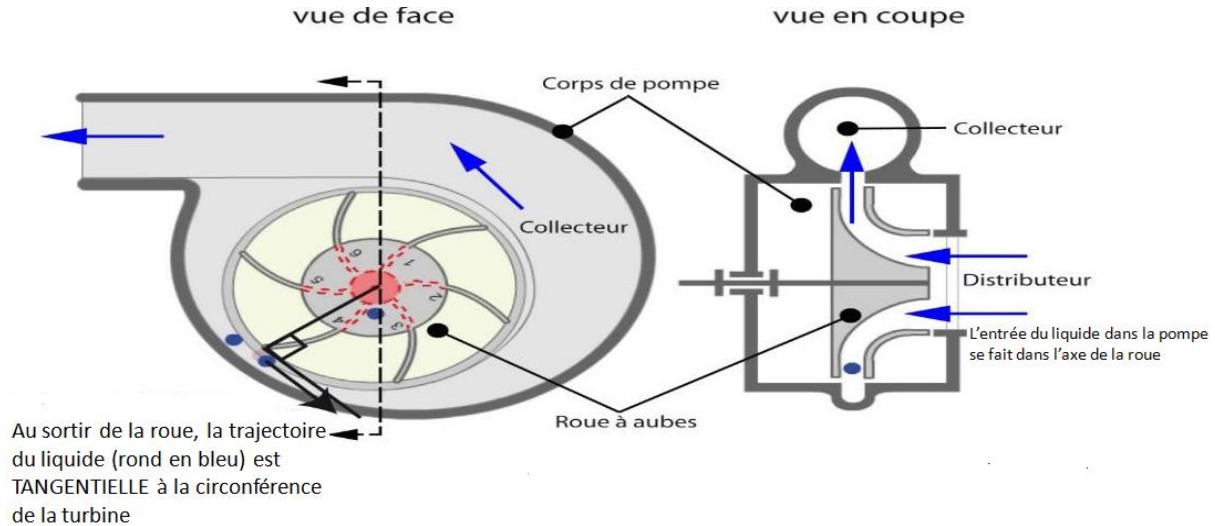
Coupe de la construction de base d'une pompe centrifuge.
